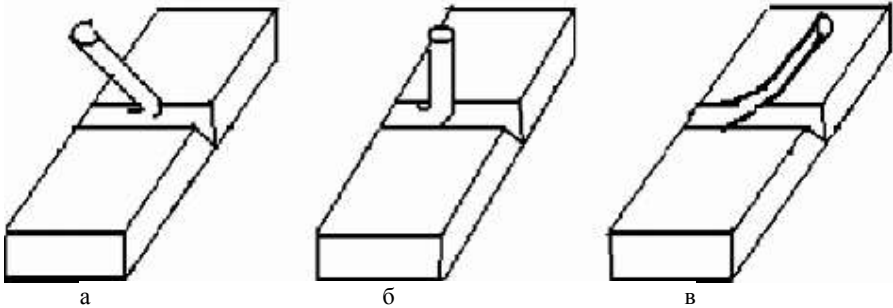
Основні типи зварних з'єднань при прутковому зварюванні
